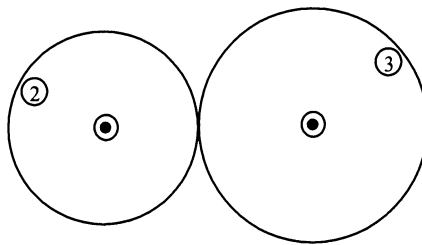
Cilindros rodantes con condición de rodadura en el contacto.
